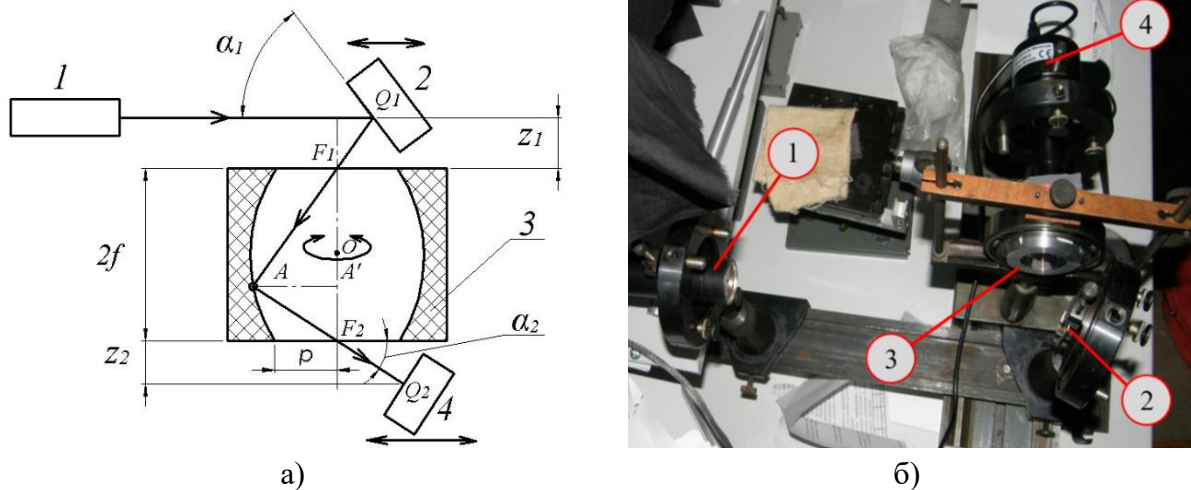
Схема пристрою (а) та загальний вигляд установки (б) для контролю параметрів робочої поверхні дзеркального еліпсоїда обертання:
